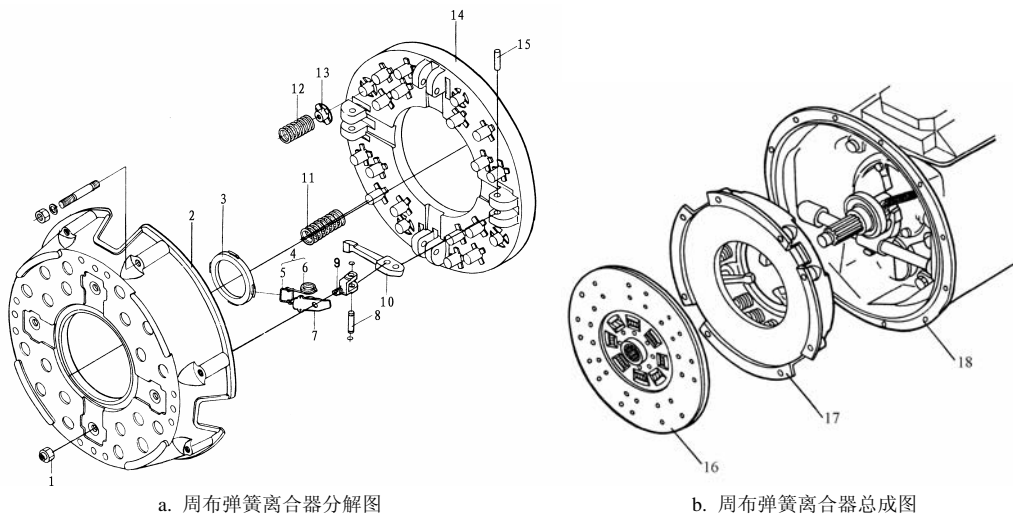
EQ 1128G 汽车单盘周布弹簧离合器结构
